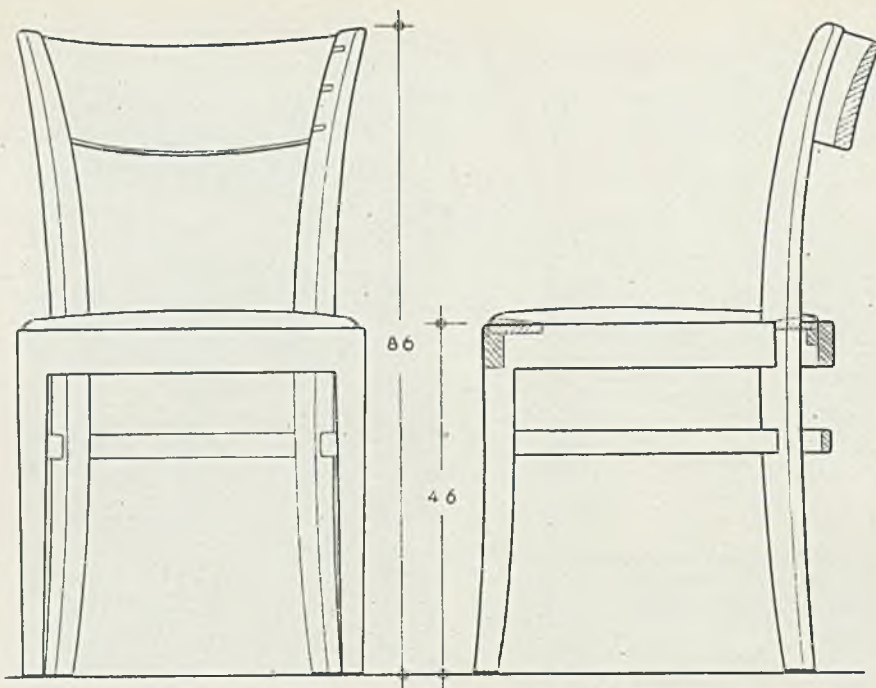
u. 86. Zargenstuhl aus geräucherter Eiche auf halbrundem Grundriß und eingelegtem Flachpolster mit Lederbezug. Man beachte die Schrägstellung der Hinterbeine, ihre Ausladung und die Führung des halbrunden Stegs, der dem Grundriß entspricht, analog dem T-Steg mit eckigem Grundriß in Abb. 83. Entwurf: N.
